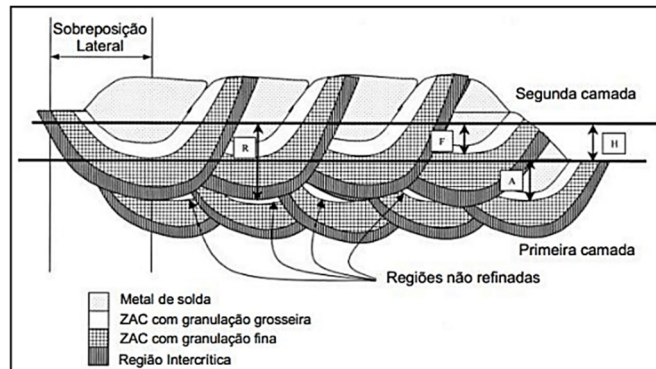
Ilustração do esquema de soldagem a arco elétrico com eletrodos revestidos.
